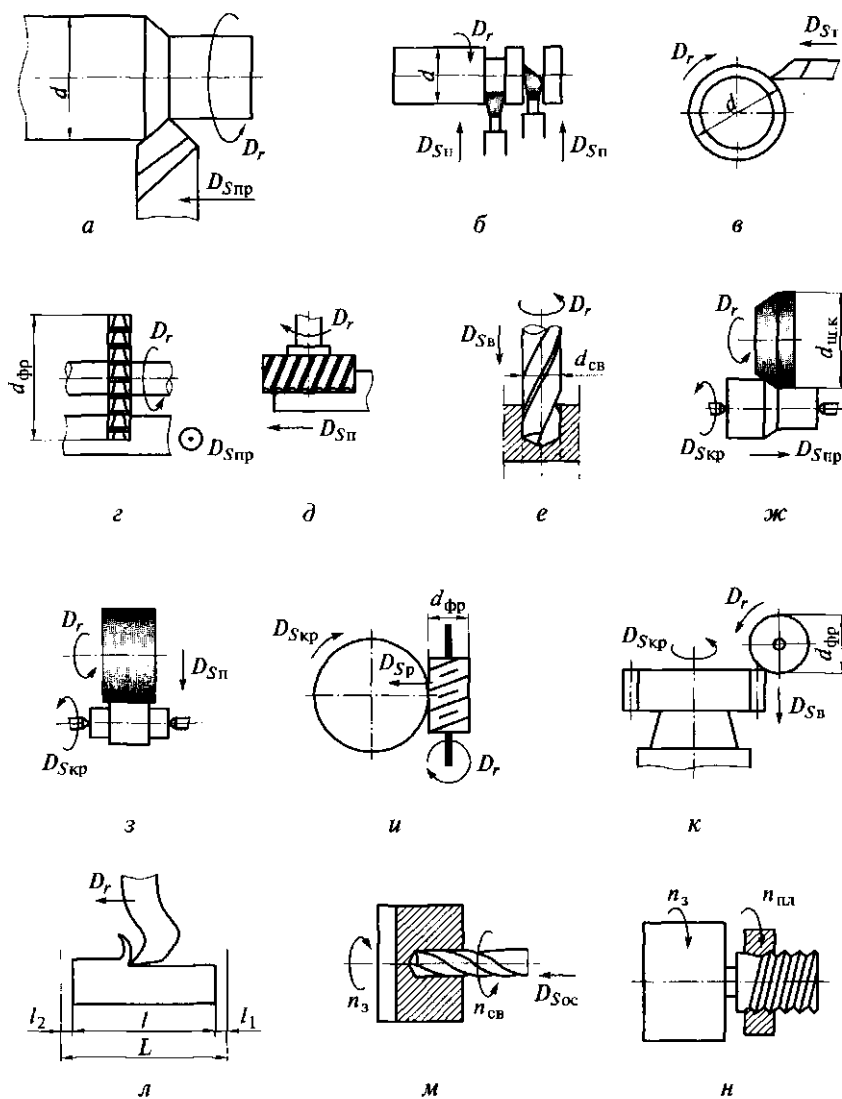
Виды главного движения и движения подачи в токарных (а, б, в), фрезерных (г, д), сверлильных (е), шлифовальных (ж, з), зубофрезерных (и, к), строгальных (л) станках и токарных автоматах (м, н):
